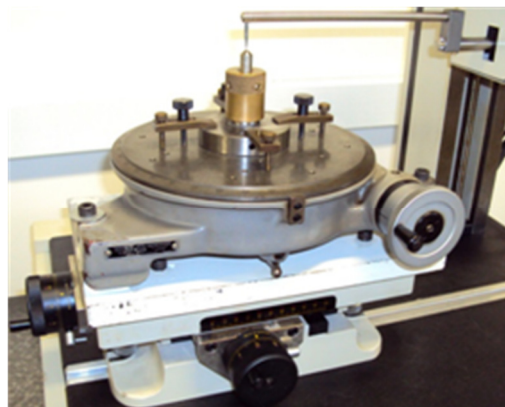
Penetrador Rockwell C posicionado na máquina de medição de perfil.
